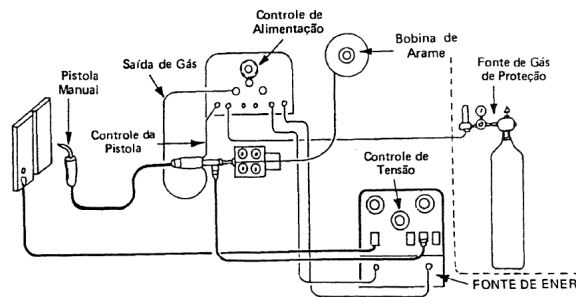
Equipamentos de Soldagem - Fonte: Apostila FBTS
